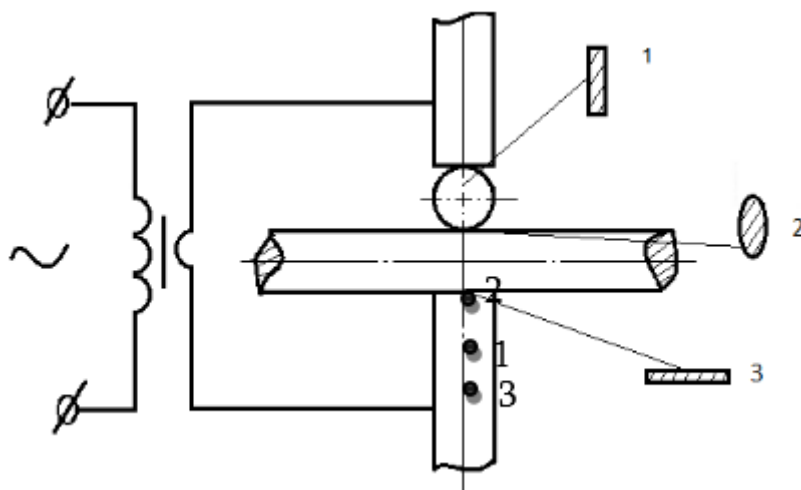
Схема контактной сварки перекрещивающихся стержней и очертания контурных площадок: 1, 3 – между электродом и стержнем; 2 – между стержнями
